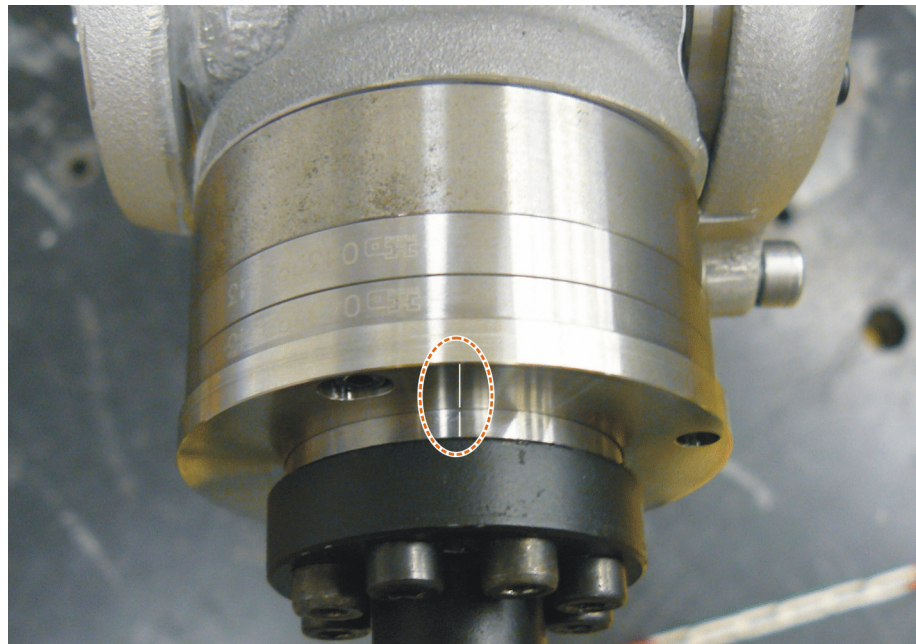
Position de calibration d'A6 - vue avant d'en haut
